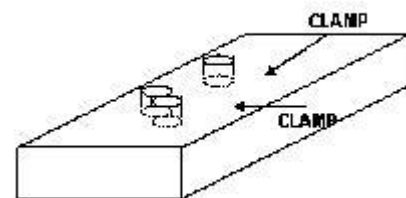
Ejemplo de diseño de plantilla (Drill fixture).
